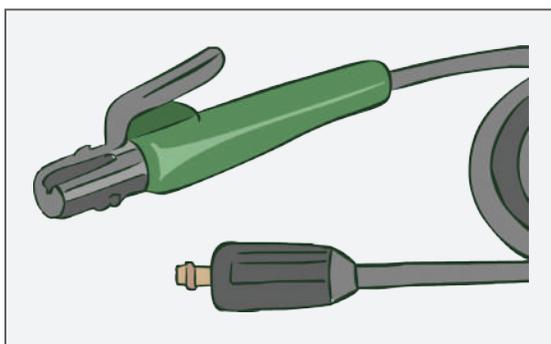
A - Cabo de soldagem unido ao porta-eletrodo
